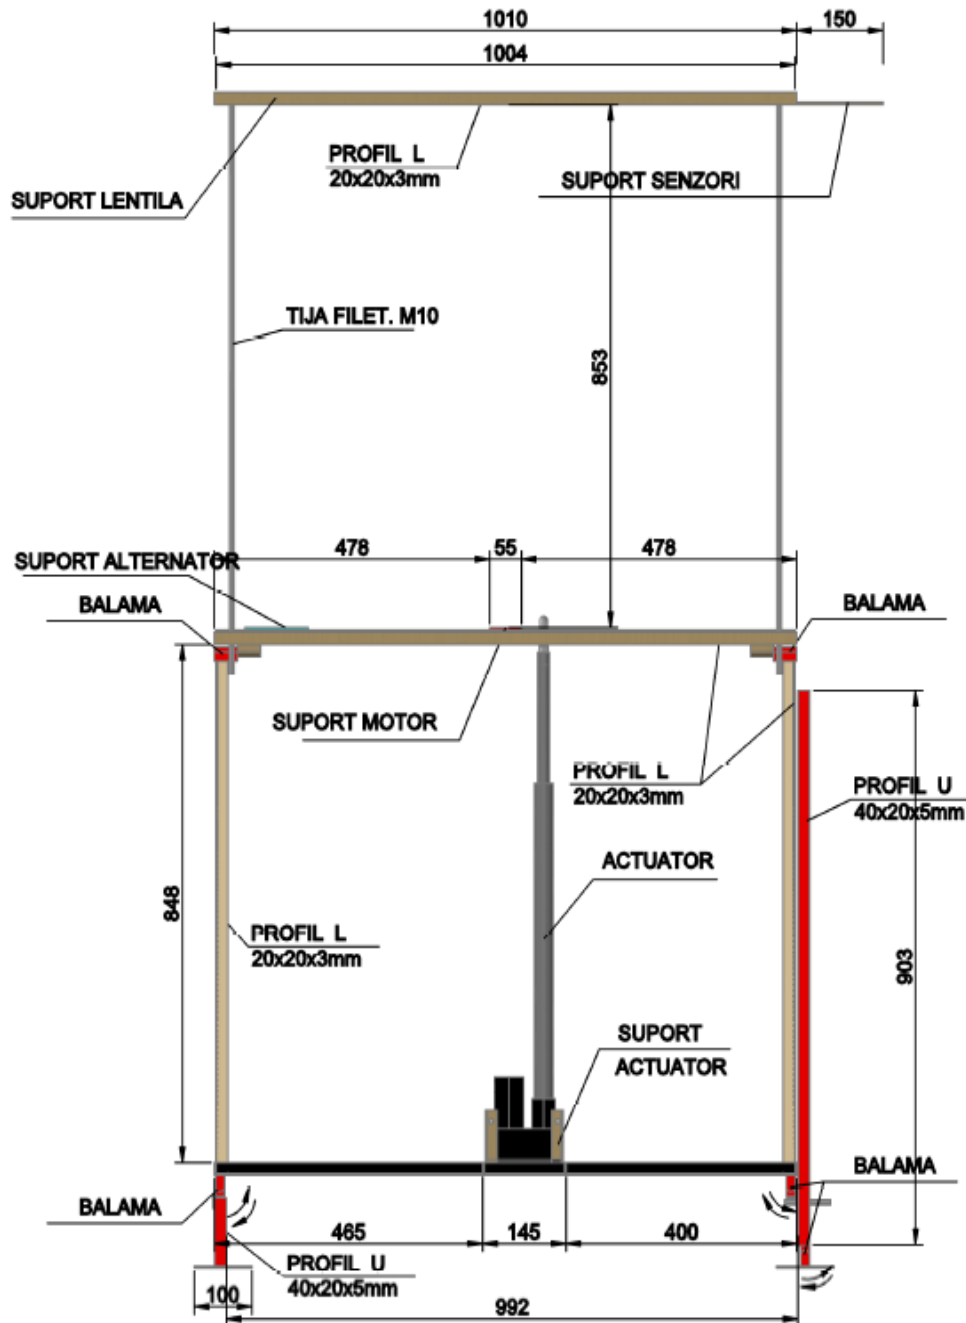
Instalație experimentală prototip 2 - Cadru suport vedere laterală
